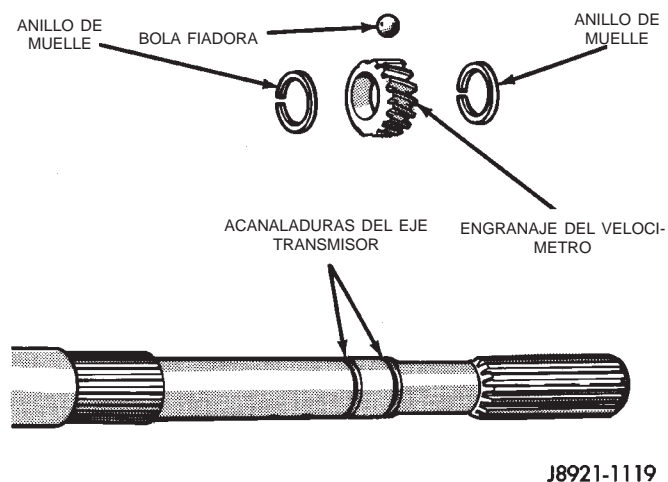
Conjunto del engranaje propulsor del velocímetro
